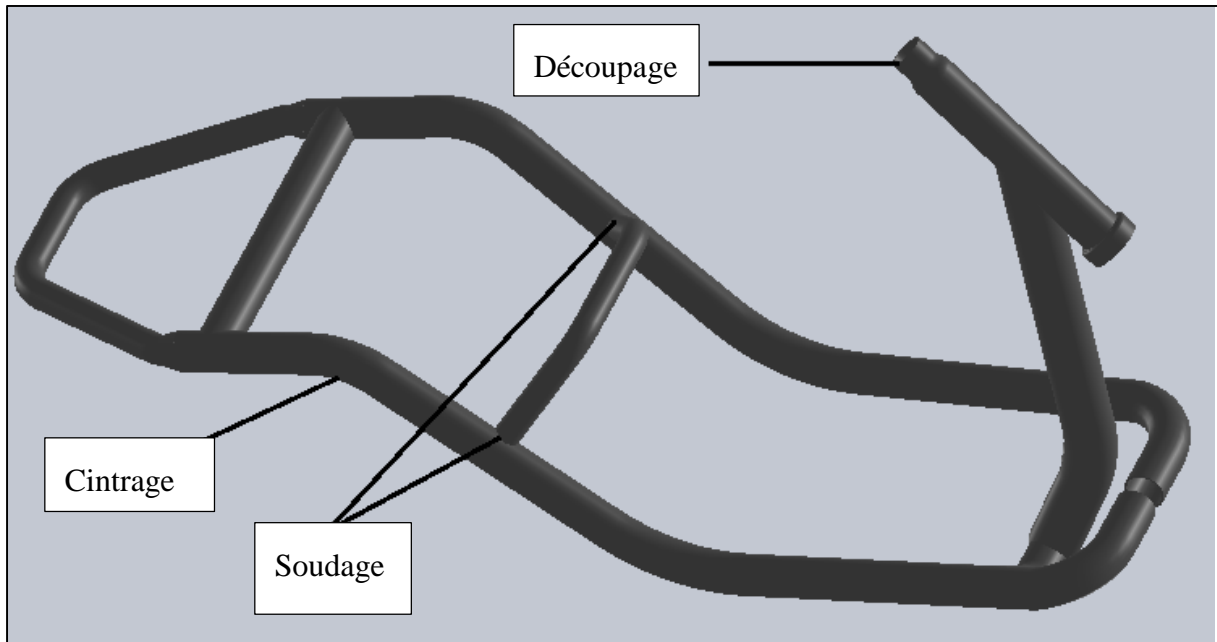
Procéder faisant partie de la fabrication du châssis de scooter
